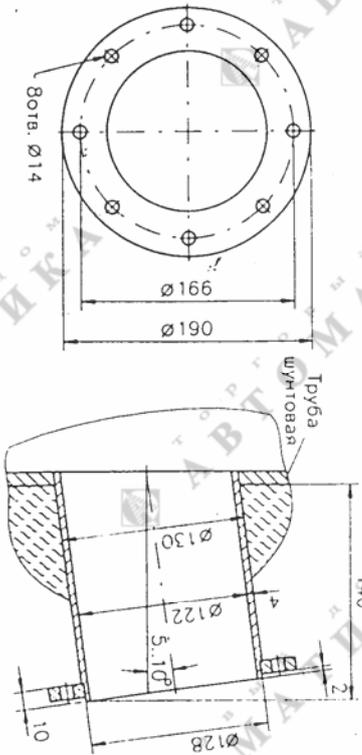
Габаритно-установочный чертеж блока силового газоснализатора АДГ-210
